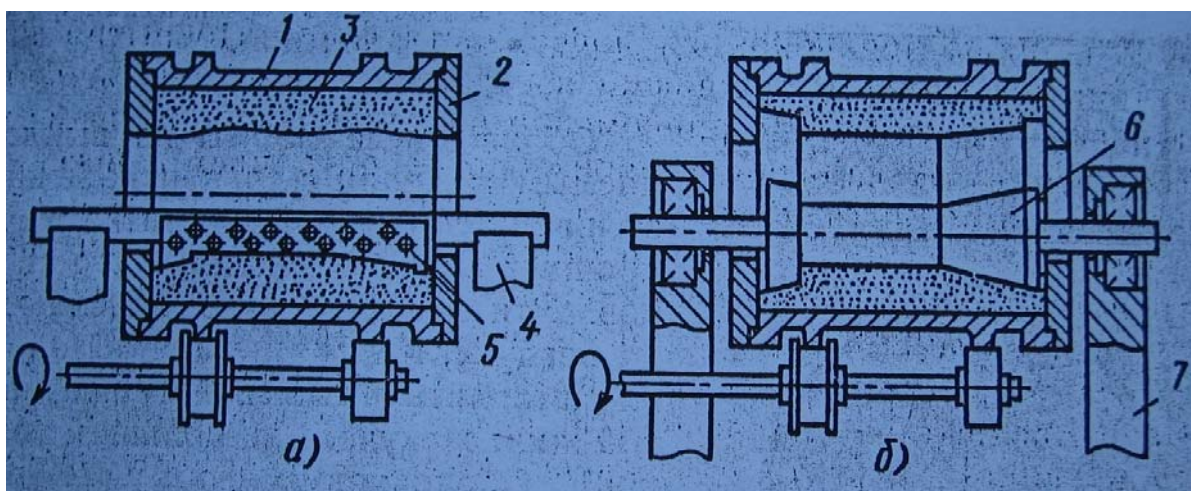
Футеровка форм накаткой. 1- изложница, 2- крышка, 3- формовочная смесь, 4- опора шаблона, 5- шаблон, 6- ролик, 7- опора ролика, а – шаблоном, б - роликом.
